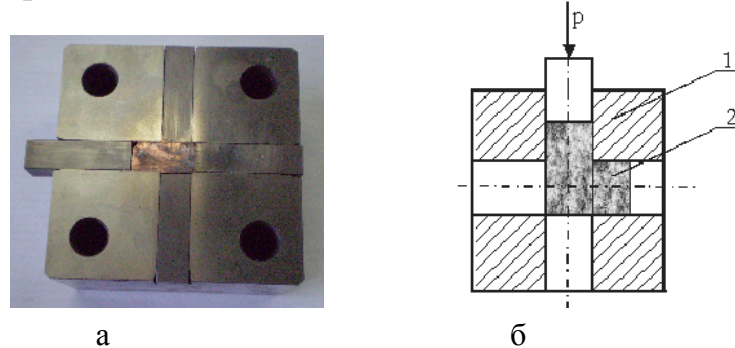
Установка для РКУ-прессования: фото матрицы – а; эскиз штампа – б: 1 – матрица; 2 – образец
